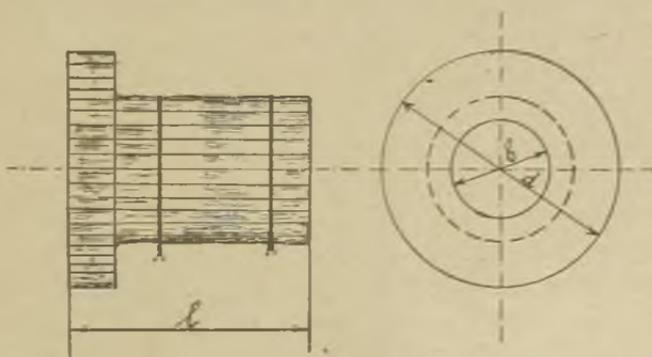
Abgreifen der Grundmaße zur Berechnung der Kollektorlamellen.
